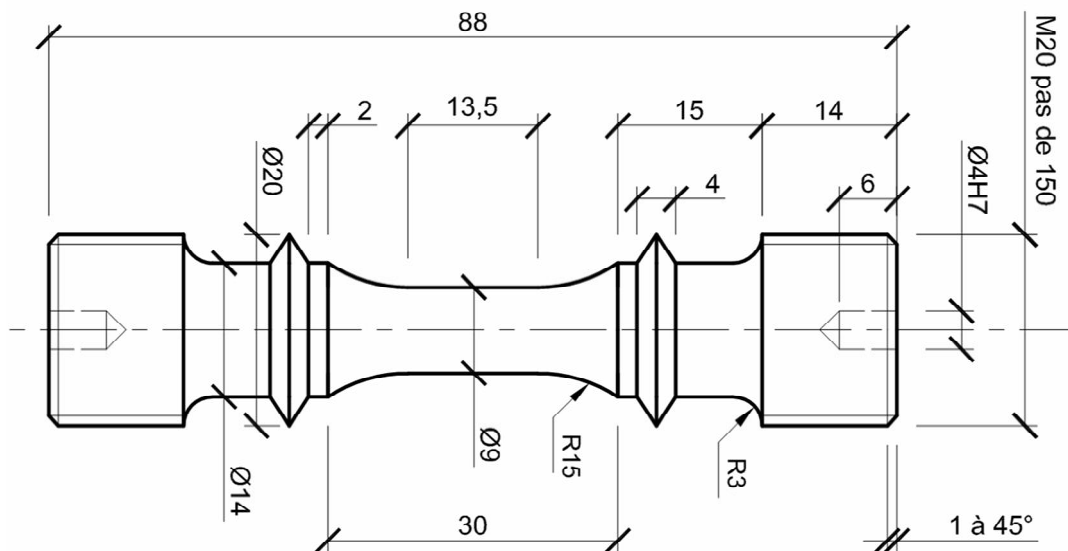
Géométrie des éprouvettes de fatigue oligocyclique (en mm).
